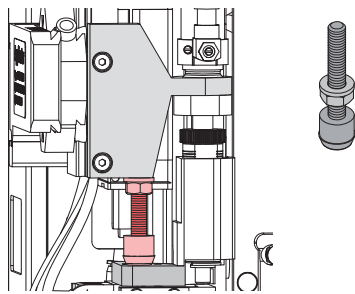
Anschlag kpl. (Stempelbaugruppe)
